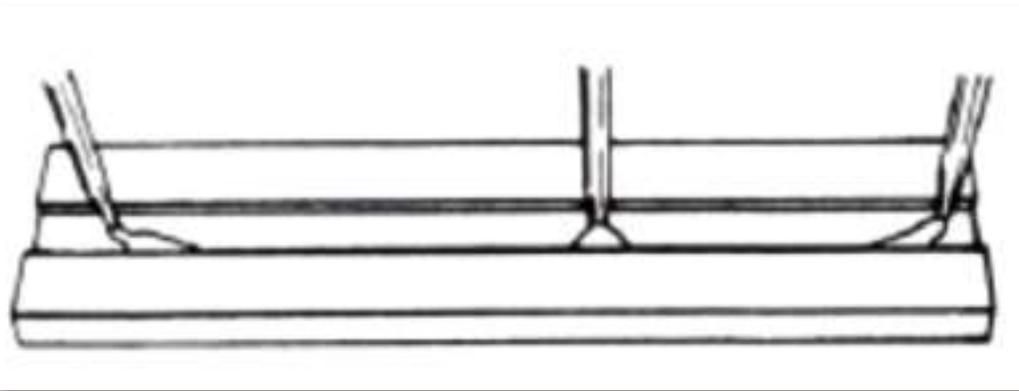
Fenómeno de sopro magnético nos extremos da peça a soldar.
